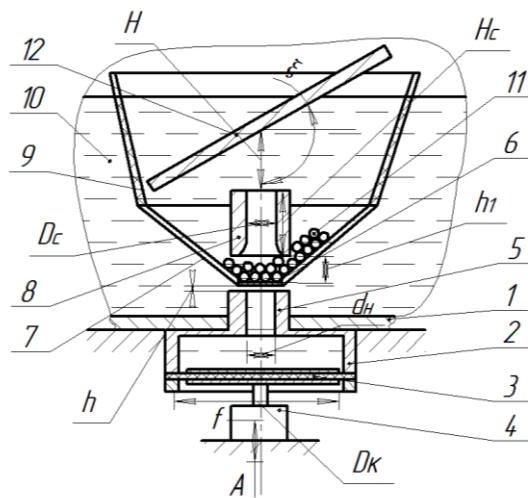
Схема моделі робочого органу вібраційної машини для очистки забруднень потоком твердих часток: 1 – корпус ванни; 2 – камера пульсації; 3 – мембрана з дисками; 4 – вібропривід; 5 – насадка; 6 – сітка; 7 – короб для збору твердих частинок; 8 – сопло; 9 – сітка; 10 – м'яча рідини; 11 – тверді частинки; 12 – поверхня, що очищується; H – відстань від сопла до поверхні, що очищується; H_c – висота сопла; h – відстань від насадка до сітки; h_1 – відстань від сітки до сопла; d_n – діаметр насадка; D_k – діаметр камери пульсації; D_c – діаметр сопла; f – частота коливань віброприводу; A – амплітуда коливань віброприводу
